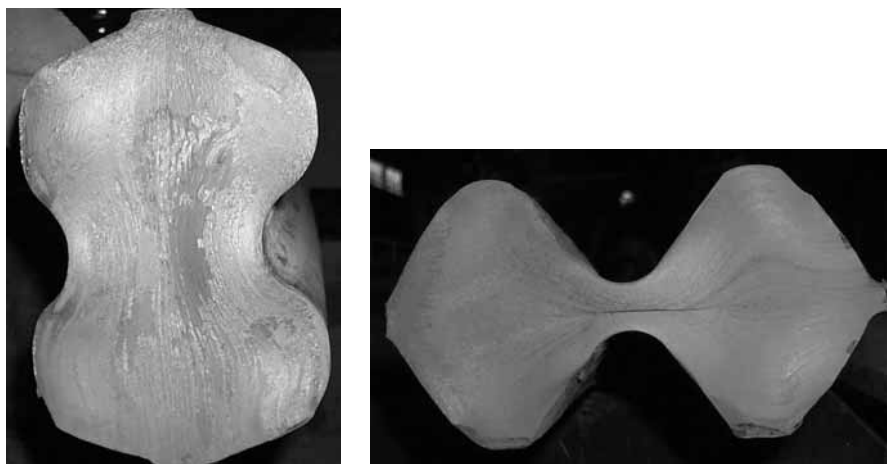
Внешний вид поперечного сечения заготовки при разделении (2-слиттинг)
